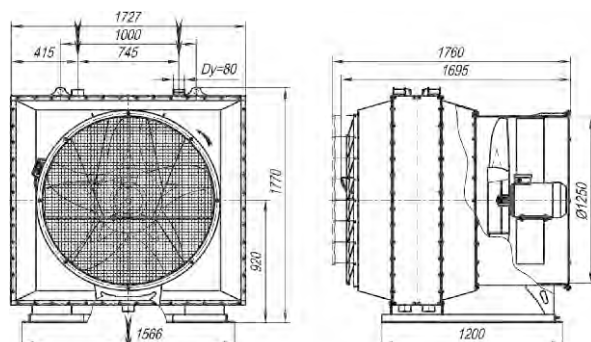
Габаритные и присоединительные размеры агрегата А02-50 на базе двух паровых воздухонагревателей КП 3-12-СК-01 ХЛЗ.
